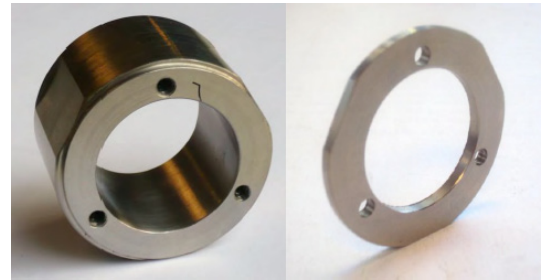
Ensamblaje parte inferior del conformador de bumps
